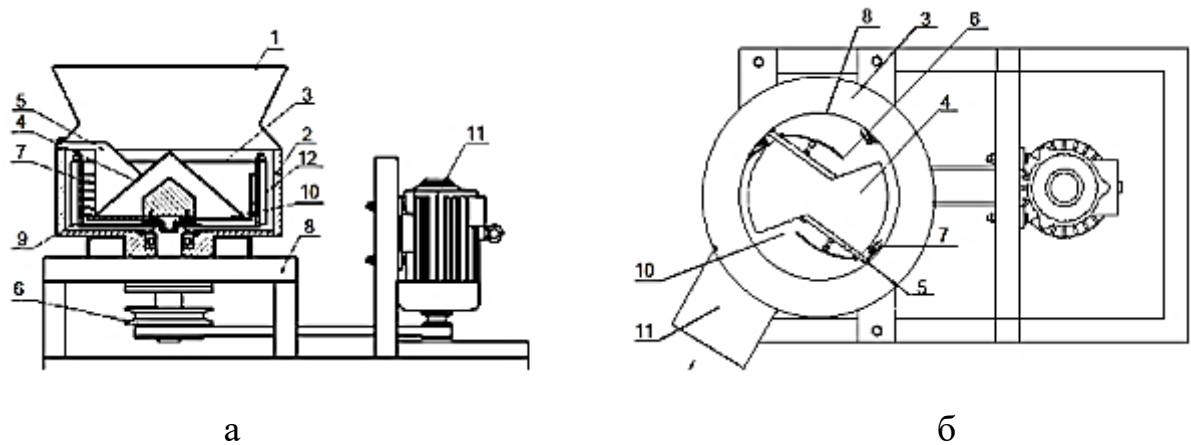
Схема подрібнювача коренеклубнеплодів: а – загальний вигляд, б – вид А-А: 1 – вікно завантажувальне; 2 – корпус; 3 – ротор; 4 – конус напрямний; 5 - протиріжуча пластина; 6 – передача клинопасова; 7 – ножі горизонтальні; 8 – рама; 9 – лопатки вивантажувальні; 10 - основа; 11 – електро-двигун; 12 – ножі вертикальні
